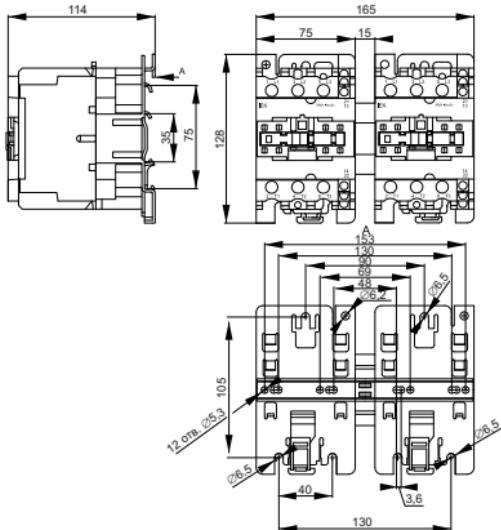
Габаритные и установочные размеры КМИ-34032, КМИ-35032, КМИ-46532 / Figure 5 – Overall and installation dimensions of KMI-34032, KMI-35032, KMI-46532
